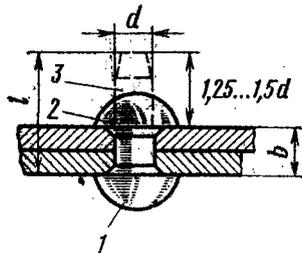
Схема для определения длины стержня заклепки для образования круглой головки:
